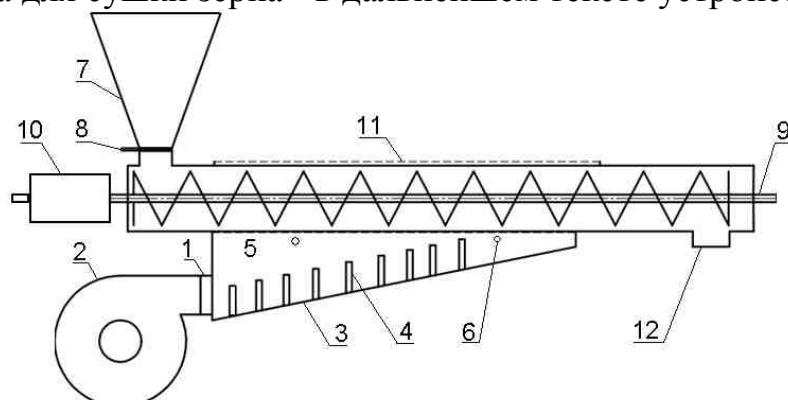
Общий вид шнекового устройства для сушки зерна.
